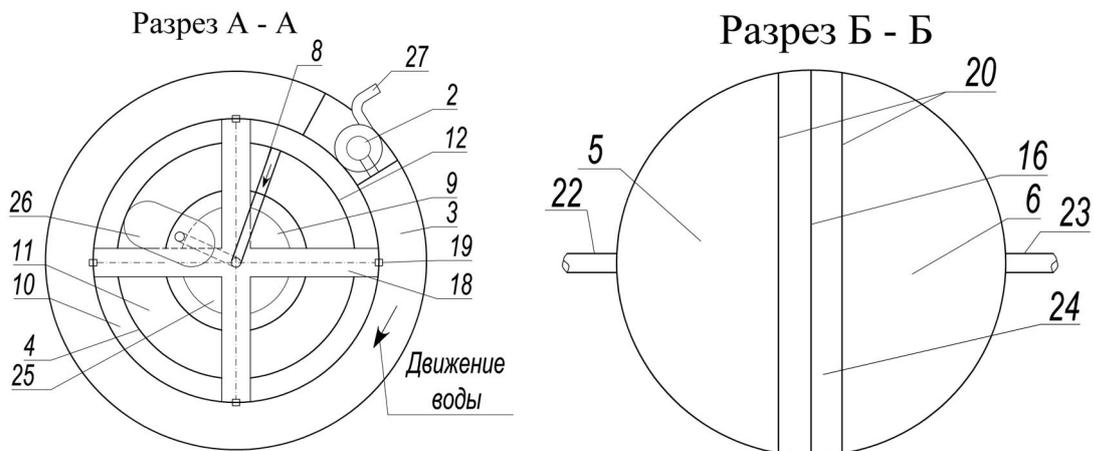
Установка для очистки сточных вод в разрезе (вид сверху)
